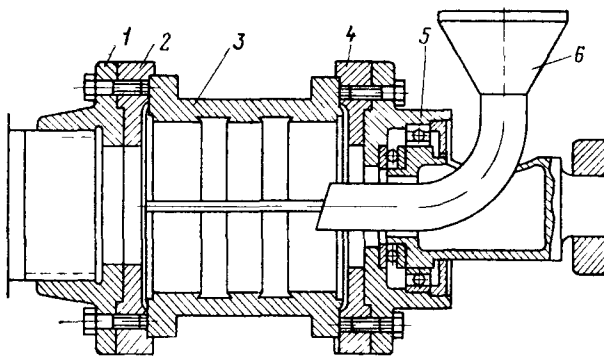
Приспособление для центробежной заливки вкладышей подшипников
